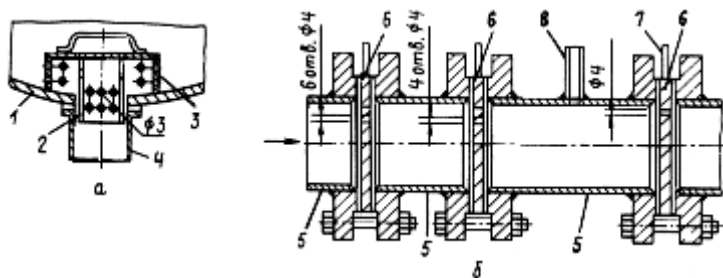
Фильтр-предохранитель (а) и дроссельное устройство (б): 1 - автоклав; 2 - патрубок фильтра; 3 - корпус фильтра; 4 - трубопровод конденсата; 5 - корпус; 6 - дроссельные шайбы; 7 - рукоятка; 8 - патрубок для присоединения пробной линии
